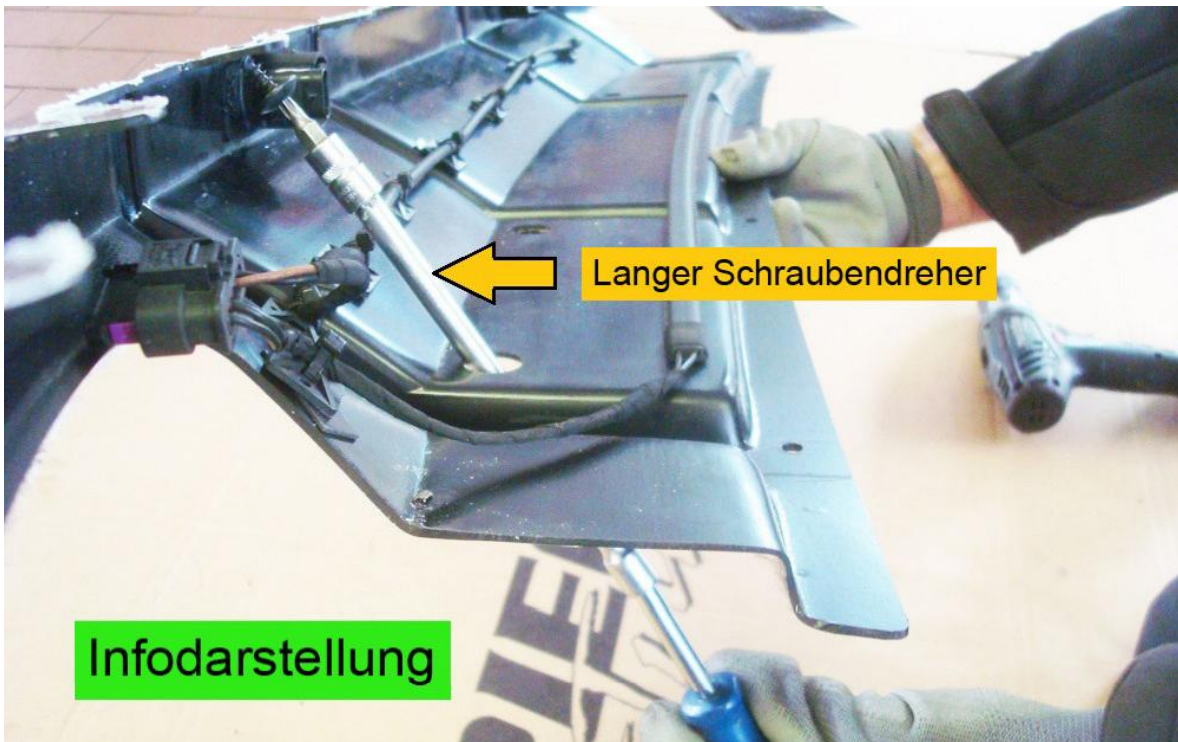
Infodarstellung für die Anbringung der 4 Stück Torxschrauben 5,0x16mm, mit denen der Heckeinsatz durch die Befestigungslaschen mit der orig. Heckstoßstange verschraubt wird. Damit die Verschraubung mit einem langen Schraubendreher möglich ist, sind am Heckeinsatz in der unteren Fläche extra 4 Stück große Bohrungen angebracht, durch diese kann man den langen Schraubendreher stecken um an die Montagepunkte zu gelangen, wenn der Heckeinsatz am Fahrzeug montiert ist.
